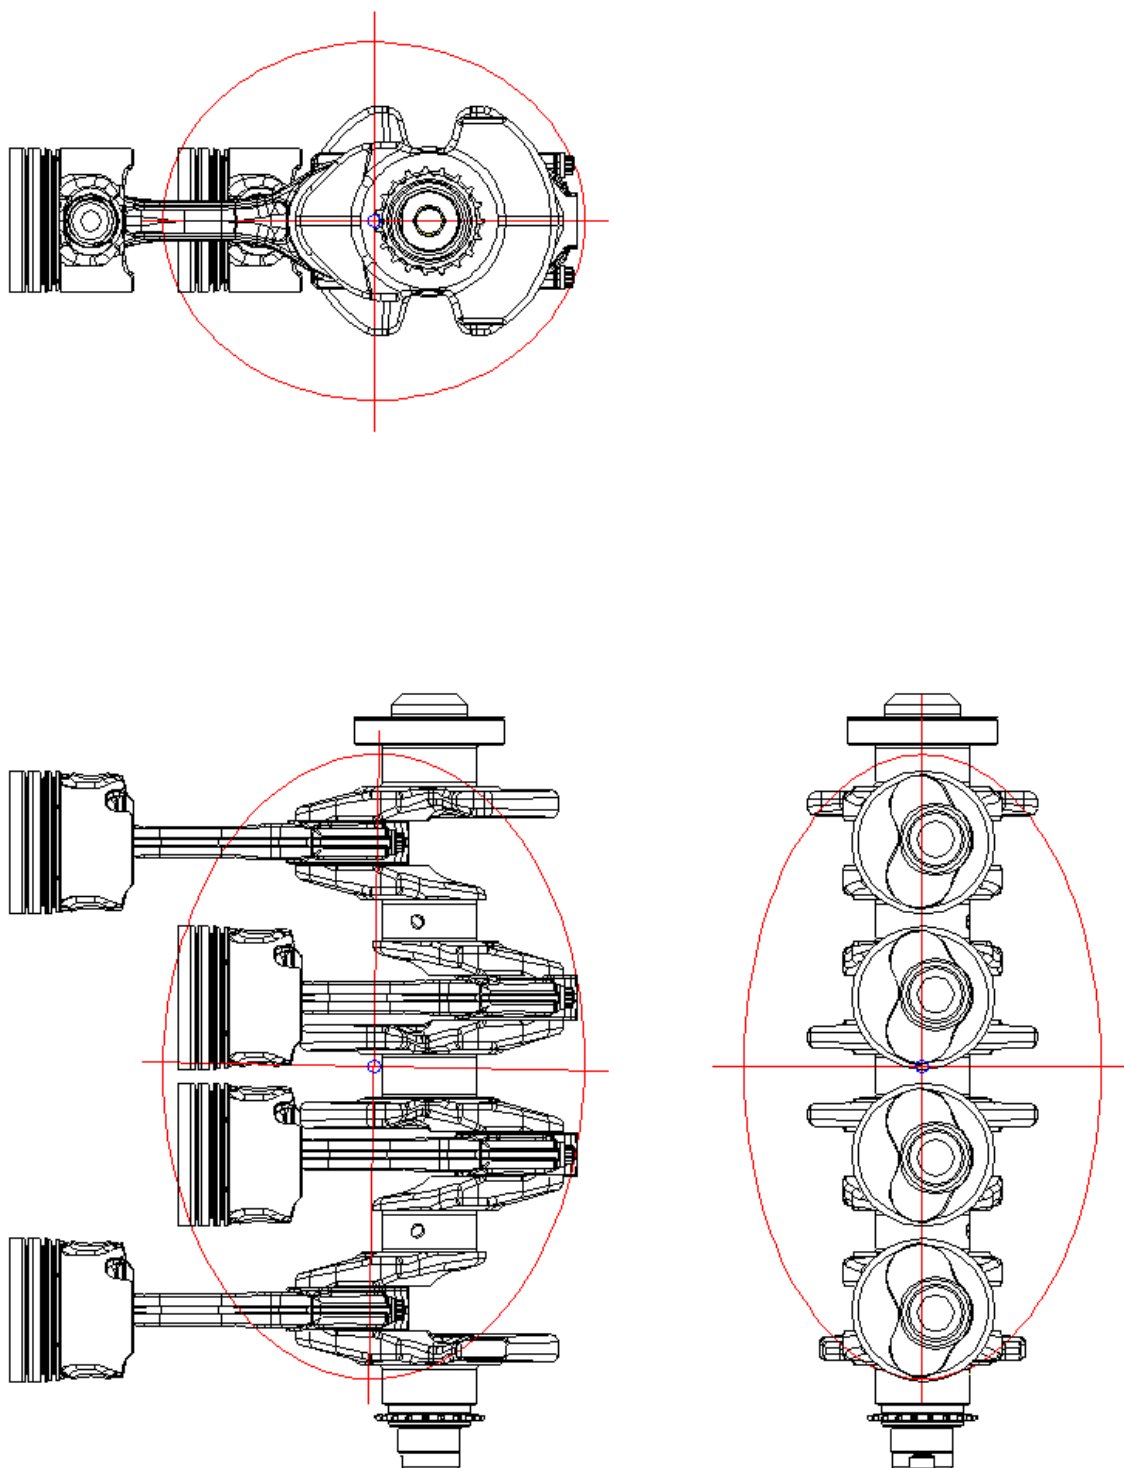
Namodelovaný klikový mechanismus motoru 2.0 103 kW TDI pro úhel $\alpha=0$ - zobrazení počátku a souřadného systému, který byl shodný se souřadným systémem celého agregátu.
